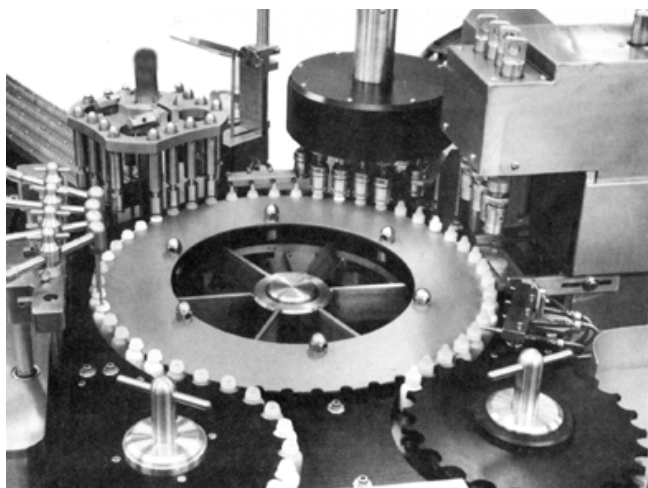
Máquina capsuladora automática rotativa por pasos (C)²
